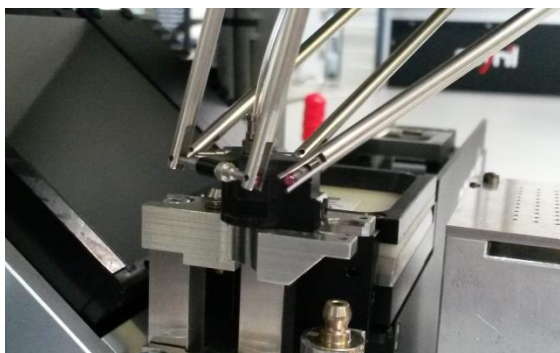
prise de la hauteur nacelle (sans outil) sur une surface plane
